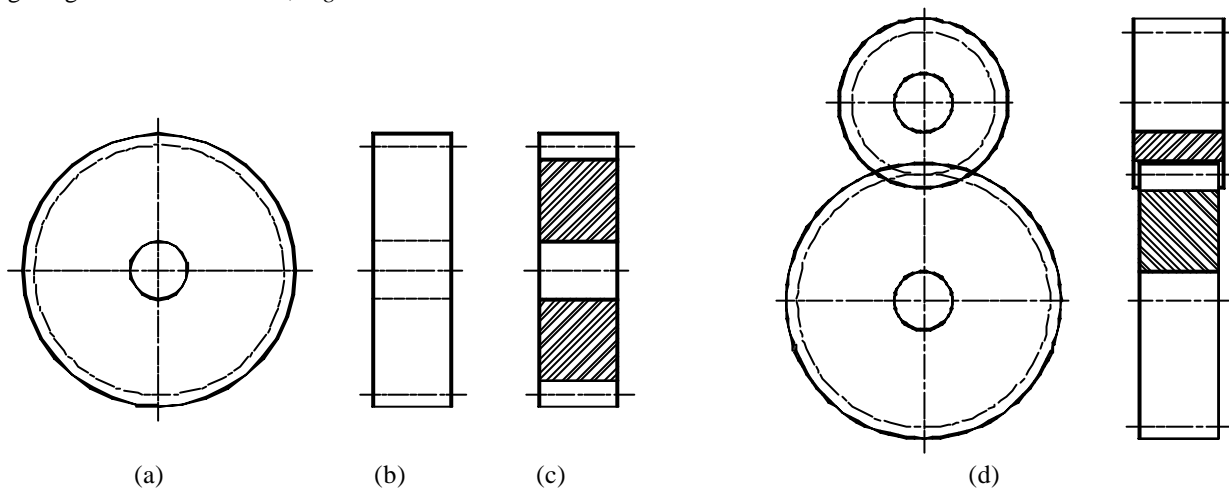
Engrenagem cilíndrica de dentes retos
